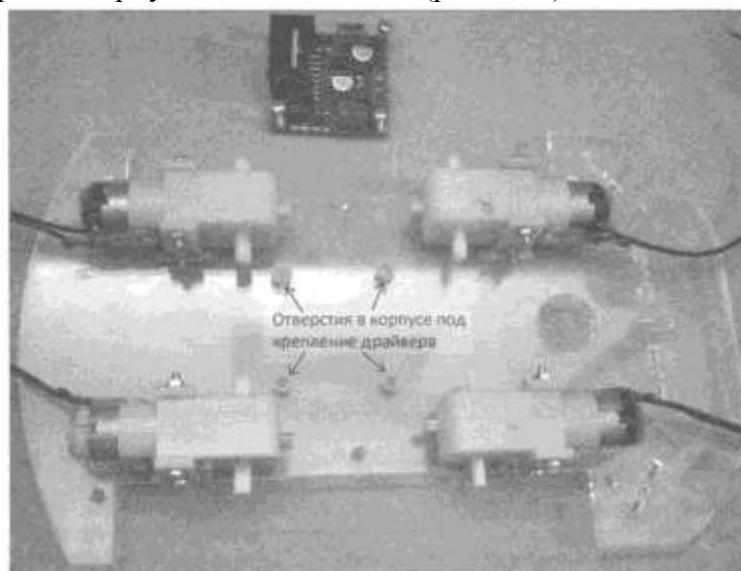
Расположение отверстий для крепления драйвера на корпусе робота
